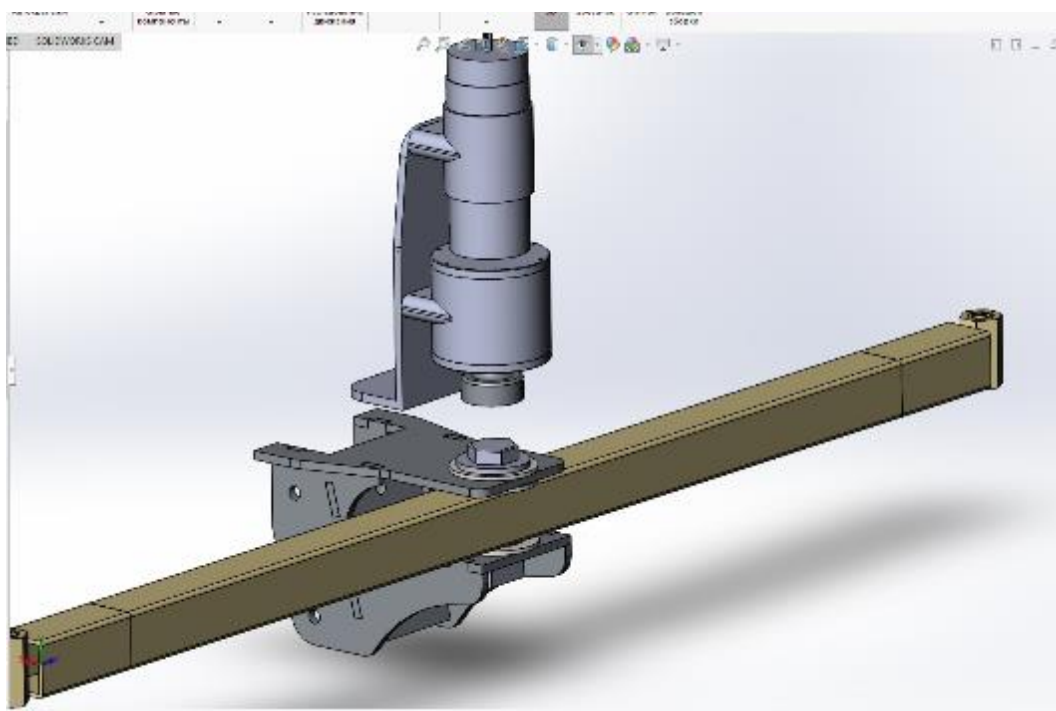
Площадка стабилизатора и привод на кронштейне, вид сверху
